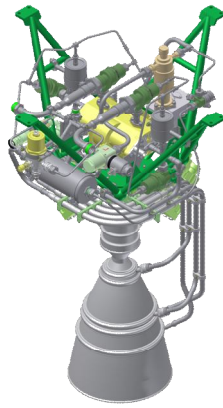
Однокамерный маршевый жидкостный ракетный двигатель РД860
